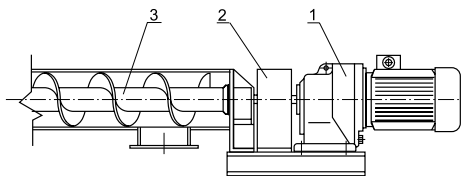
Привод винтового конвейера на базе цилиндрического соосного мотор-редуктора:
